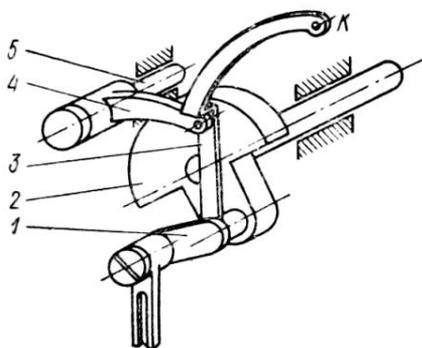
Схема четырехзвенного шарнирно-рычажного механизма нитепритягивателя
